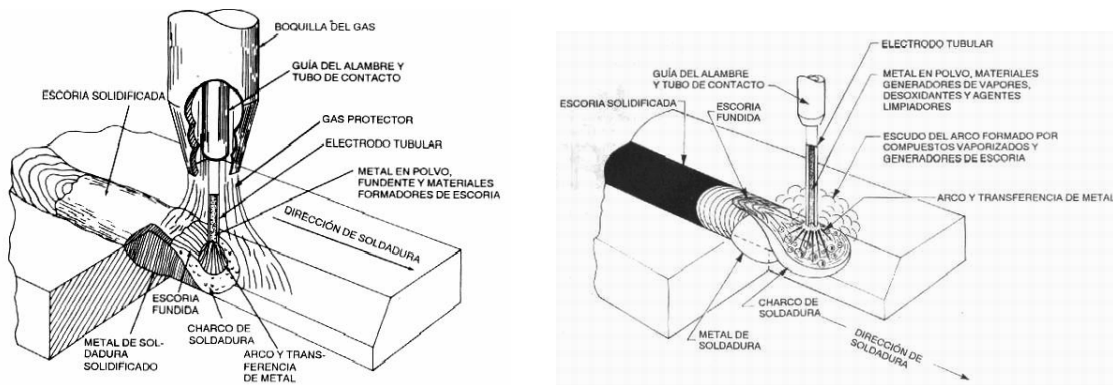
Proceso de soldadura por arco con alambre tubular con o sin protección gaseosa
